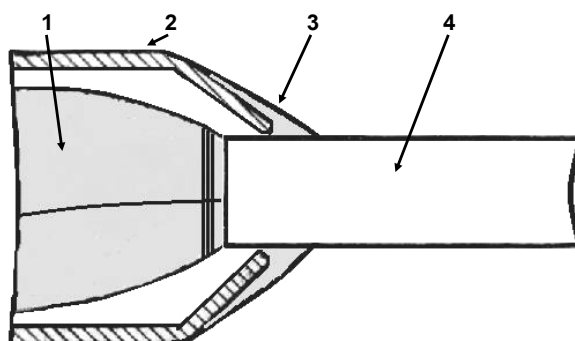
Форма шва на конусе корпуса муфты МСР в разрезе:
